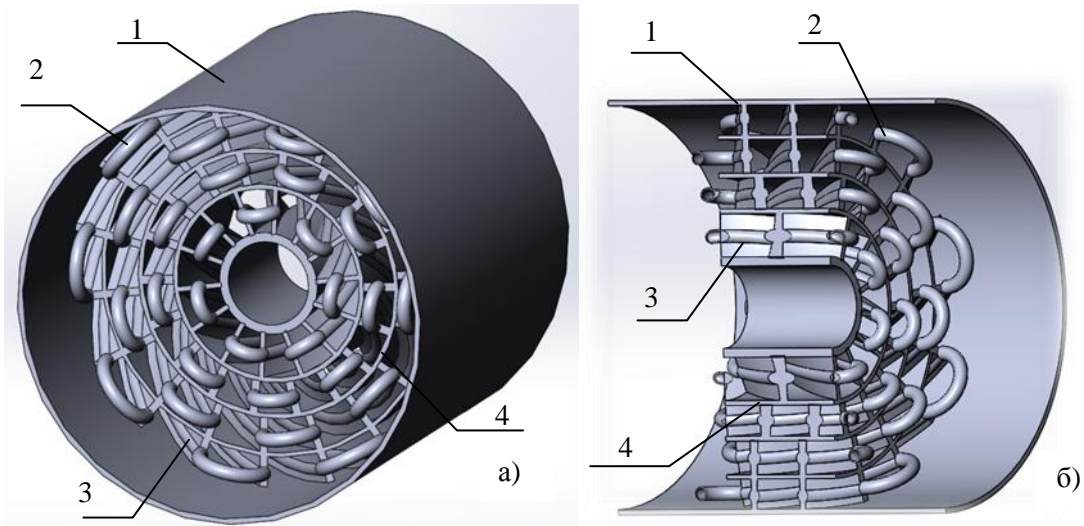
Конструкция ротационного теплообменника: а) – внешний вид проточной части; б) – разрез: 1 – внешний корпус; 2 – трубки с хладагентом; 3 – винтовые пластины; 4 – перегородки из теплопроводящего материала
